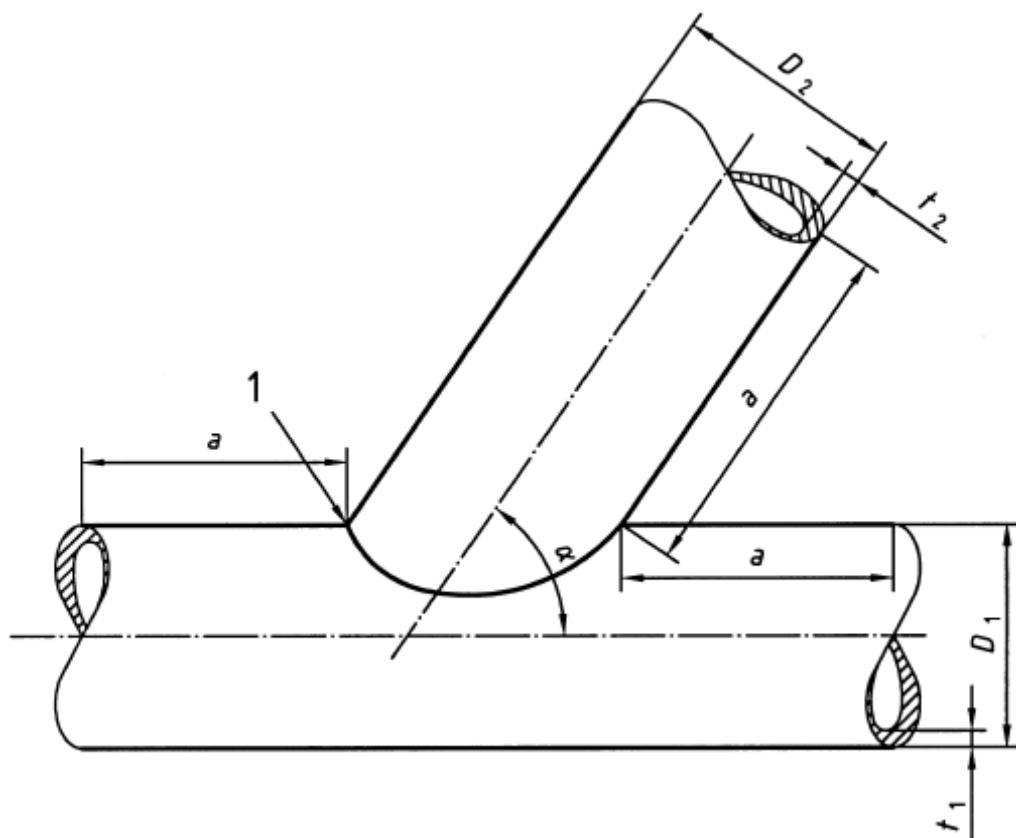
焊透管材中的对焊焊缝用试件
